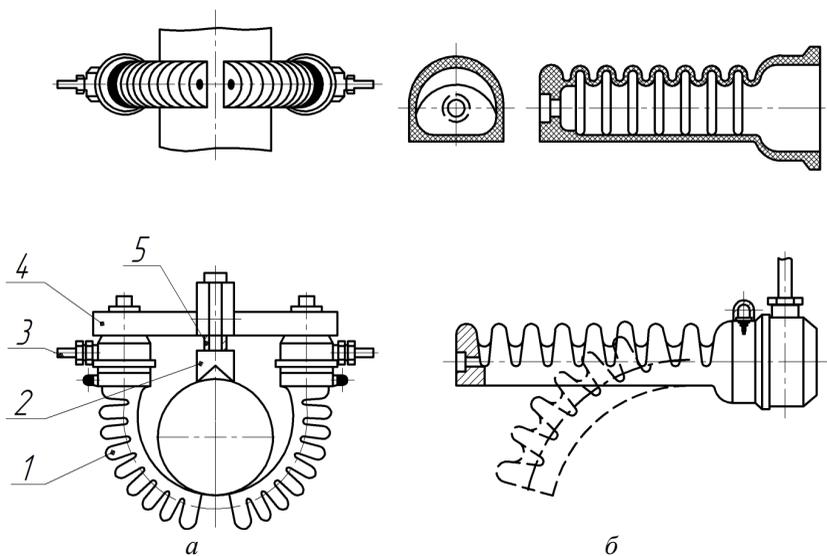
Базирующие ЗУ с изгибающимися камерами фирмы *Simrit* (Германия) для взятия объектов за наружную поверхность: *а* – схема захватывания предмета производства; *б* – конструкция эластичной камеры; 1 – камера; 2 – призма; 3 – патрубков; 4 – корпус; 5 – регулирующий держатель
